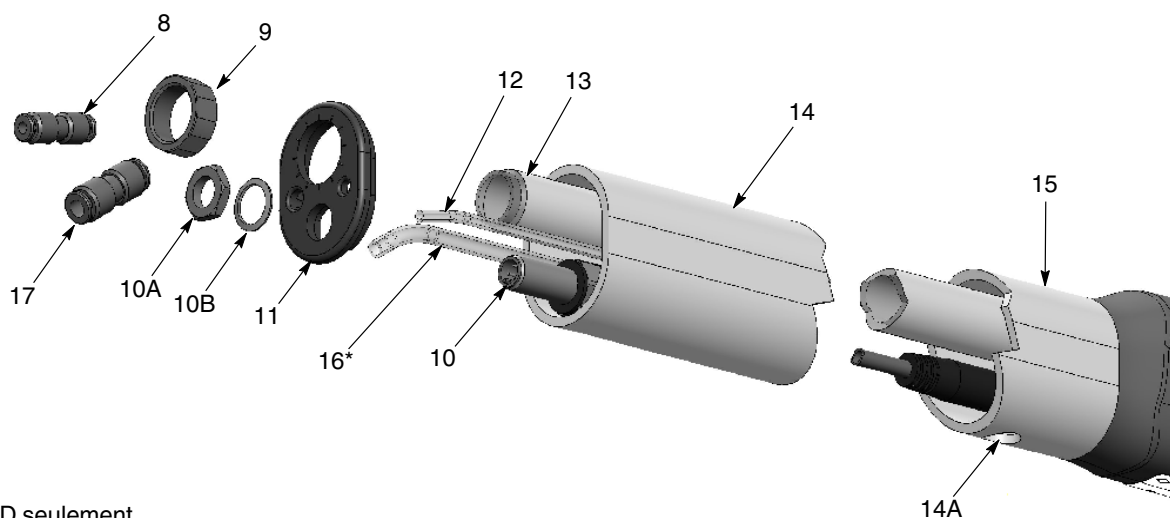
Installation du collecteur d'ions – Pistolet à fixation sur barre
